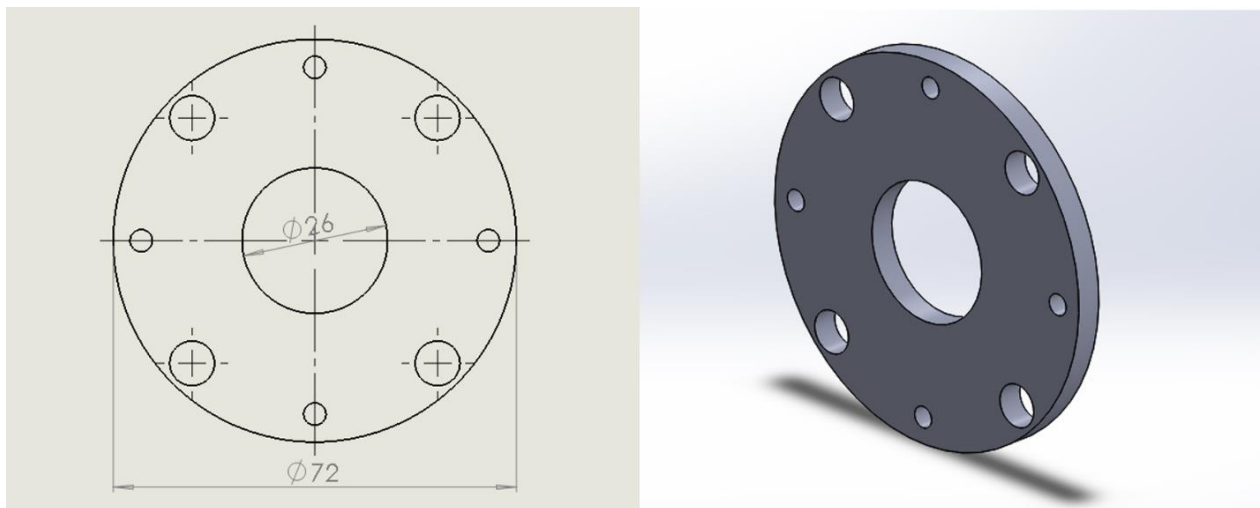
Kućište prednjeg ležaja - dimenzije i CAD model
